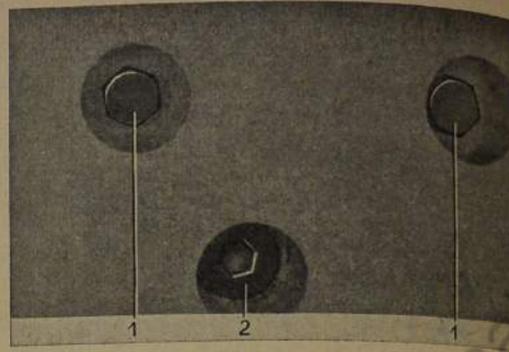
Sechskantschrauben für Getriebe am 2. Querträger abschrauben
